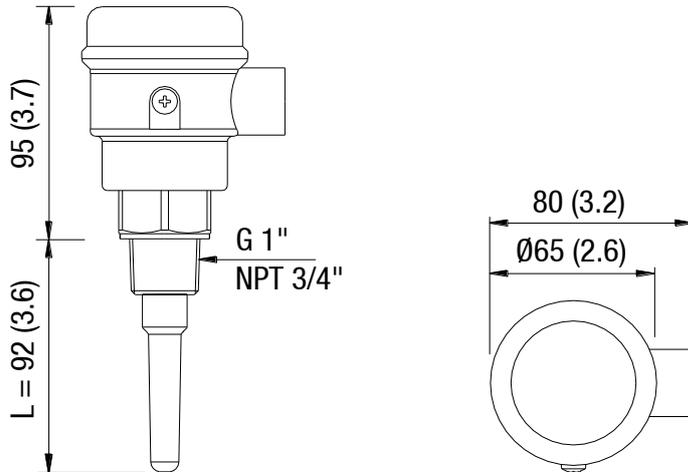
Abmessungen CN 7121, Gehäuse Ø 65 mm
